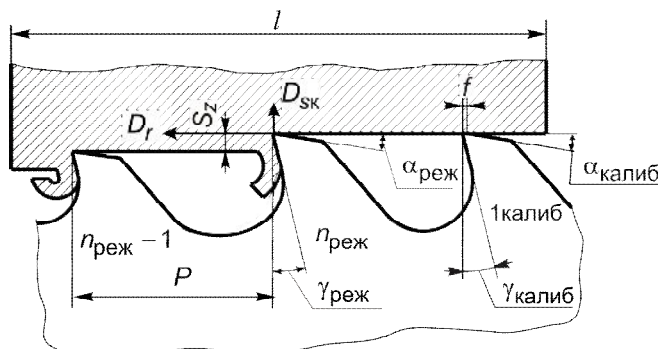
Схема срезания слоя материала зубьями протяжки; размеры и геометрические параметры режущих и калибрующих зубьев протяжки
